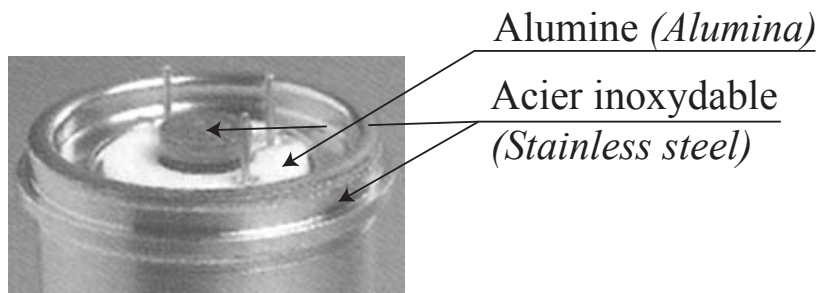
Assemblage étudié. (*Studied assembly.*)
